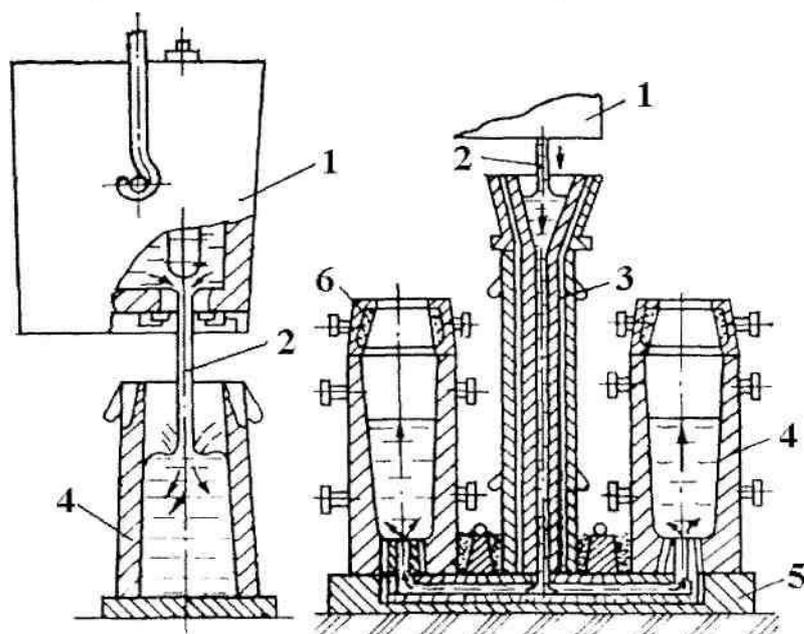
Разливка стали в изложницы: а - сверху; б - сифоном: 1 - ковш; 2- металл; 3 - центральной литник; 4 - изложницы; 5 - поддон; 6 - надставка для утепления прибыли
